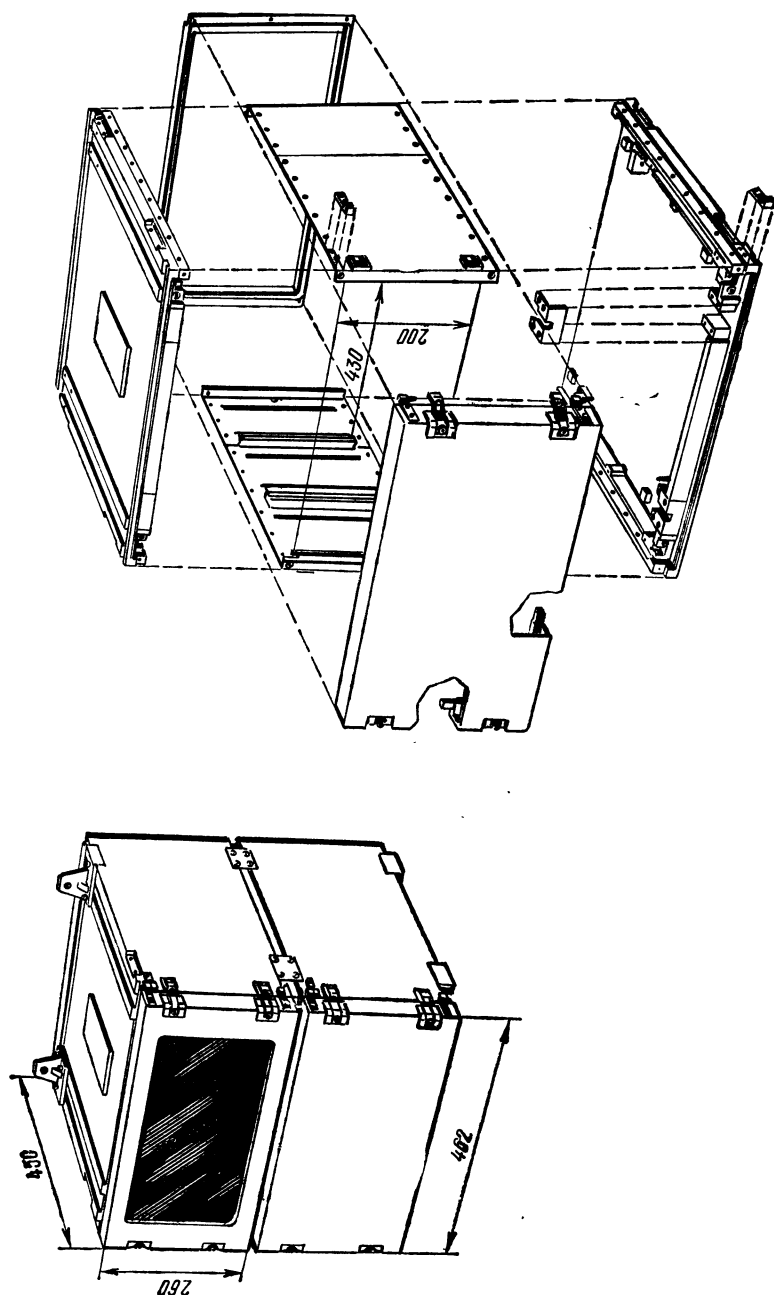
Схема конструкции приборных корпусов ВТК-11
